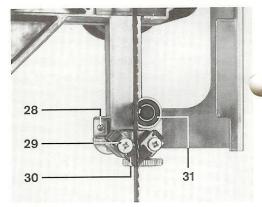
Sägeblattführung mit oberem Kugellager und oberen Führungsbacken (Abdeckblech 3 nach der Seite gedreht)
